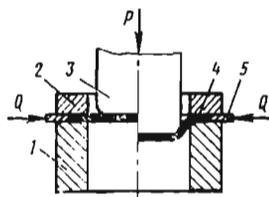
Схема вытяжного штампа с подпором фланца:
